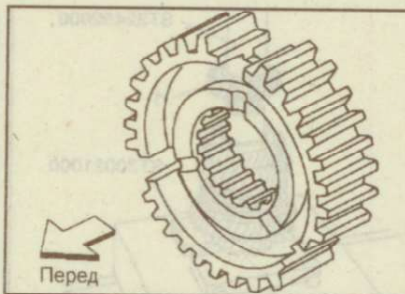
Установочное положение ступицы муфты синхронизатора
